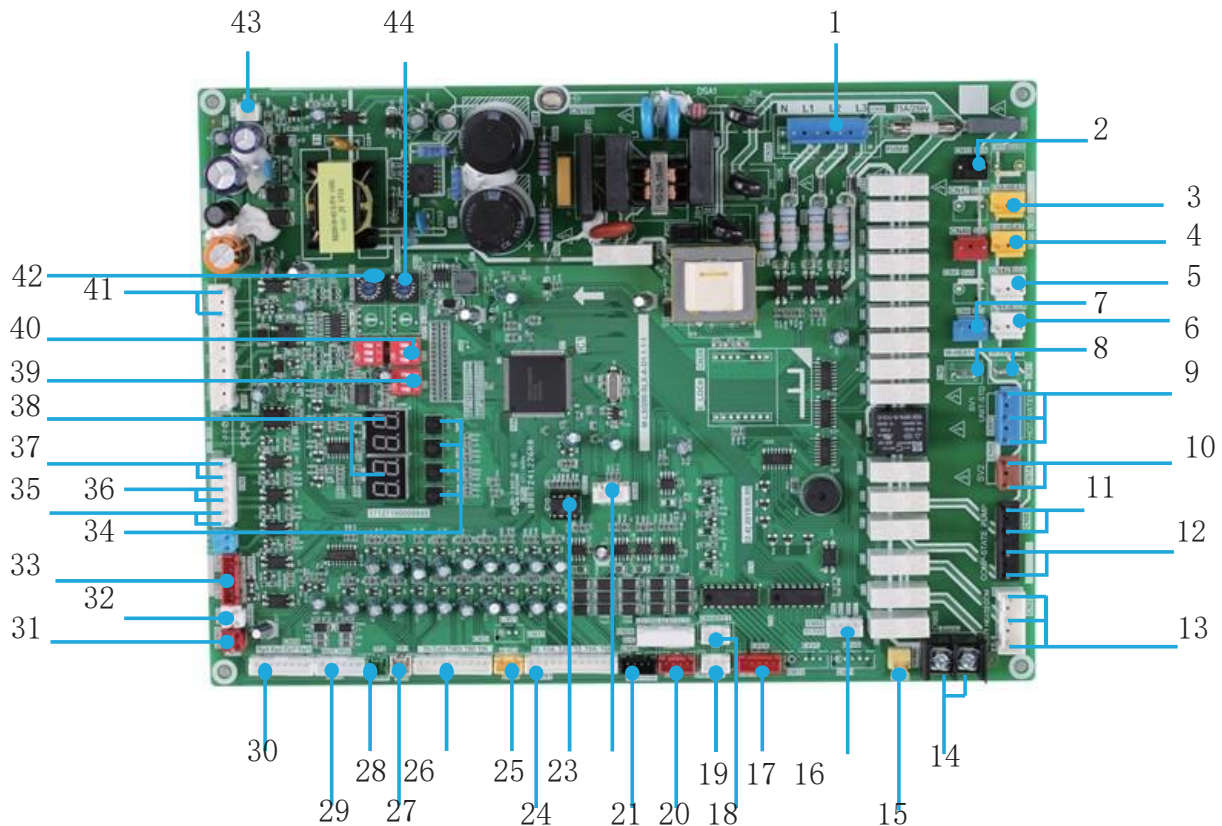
PCB principali SCV-300EBH e SCV-600EBH
